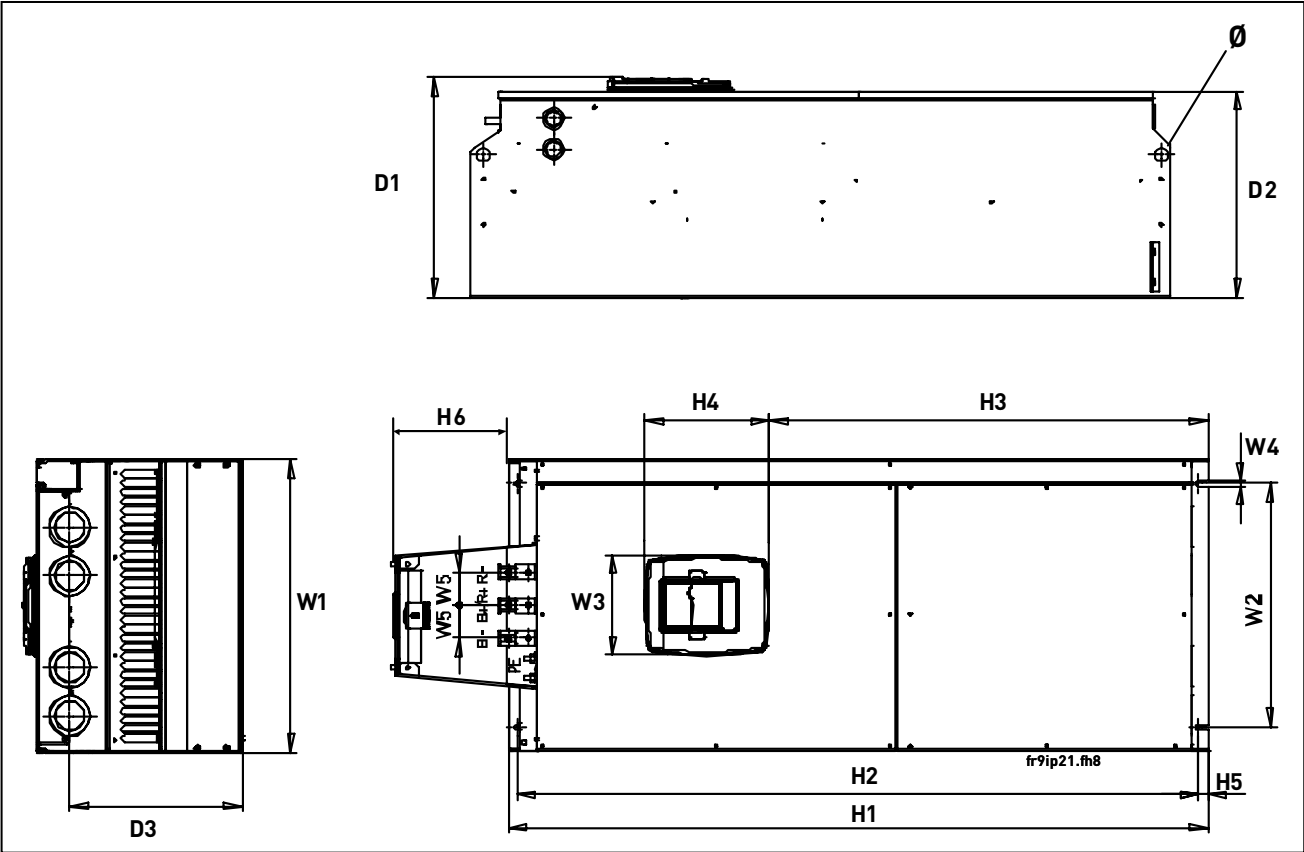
Габариты преобразователей частоты Vacon NX, типоразмер FR9
